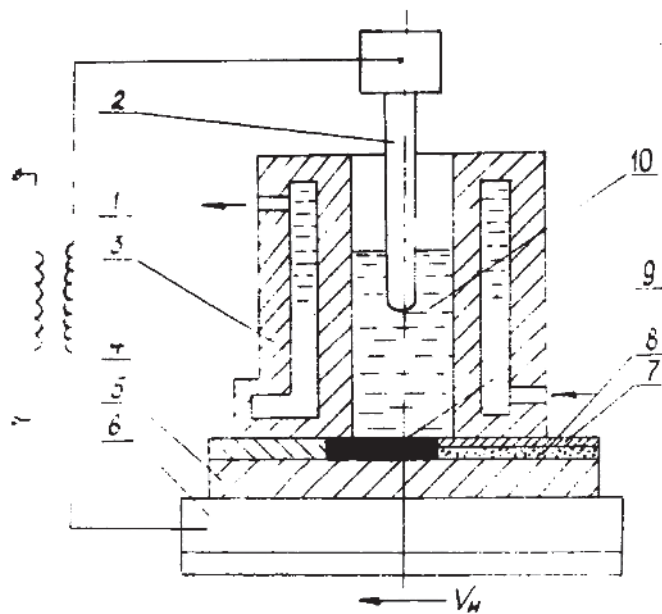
Схема способа горизонтальной электрошлаковой наплавки по слою порошкового присадочного материала (а.с. № 1235082):
